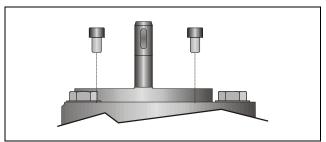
Desserrage et retrait des vis à tête cylindrique
